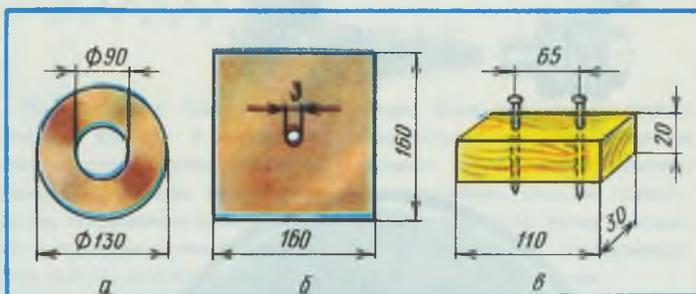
Кольцо из пластика и приспособление для его изготовления: а — готовое кольцо; б — пластина пластиковая; в — рейка-резак.
